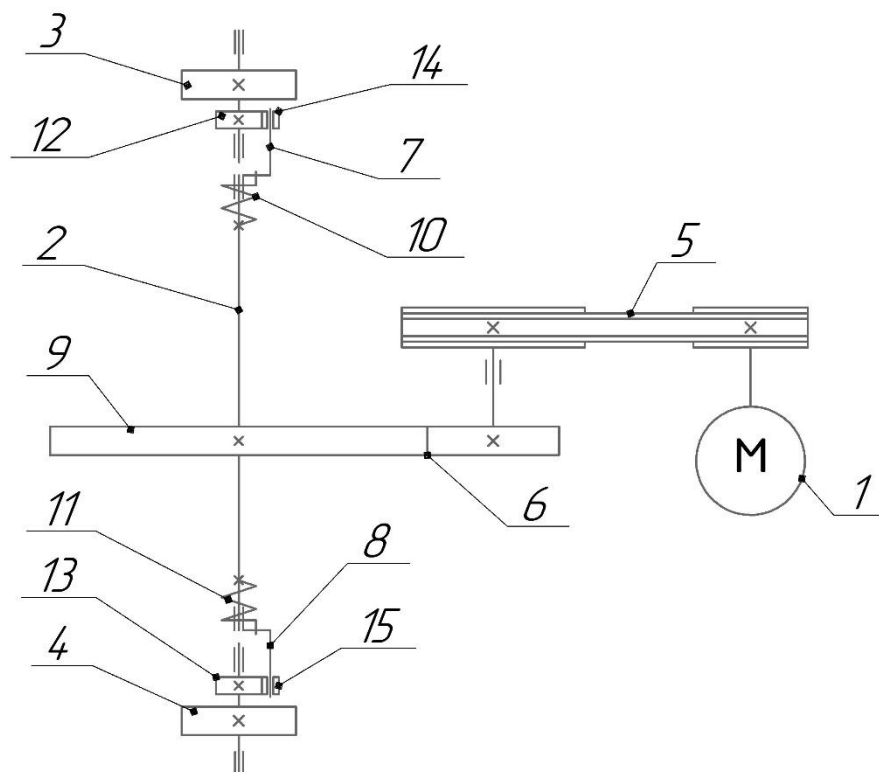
Кінематича схема привода кругловязальної машини з ПЗДН з пружинами кручення: 1 – електродвигун; 2 – приводний вал; 3, 4 – шестерні; 5 – клинопасова передача; 6 – зубчаста передача; 7, 8 – ведучі напівмуфти; 9 – зубчасте колесо; 10, 11 пружини кручення; 12, 13 – ведені напівмуфти (сонячні шестерні); 14, 15 – шестерні сателіти
